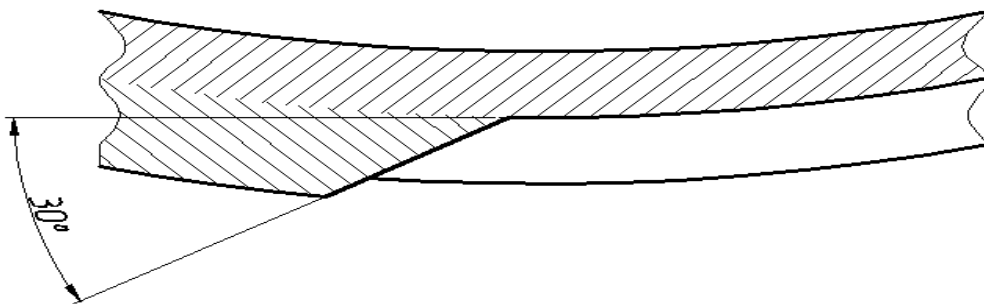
Зовнішній вигляд очищення зони початку зварювання
